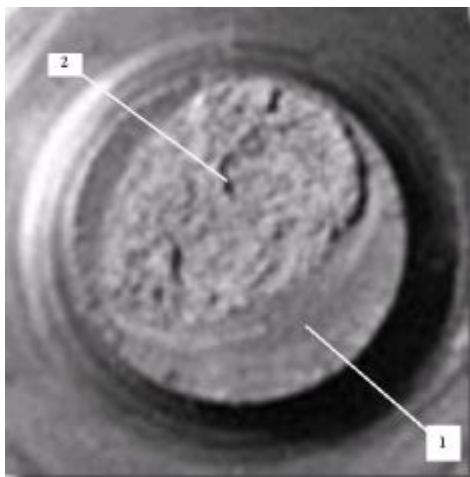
Усталостный излом шпильки крепления крышки турбины: 1 - серповидная усталостная трещина; 2 – зона долома
